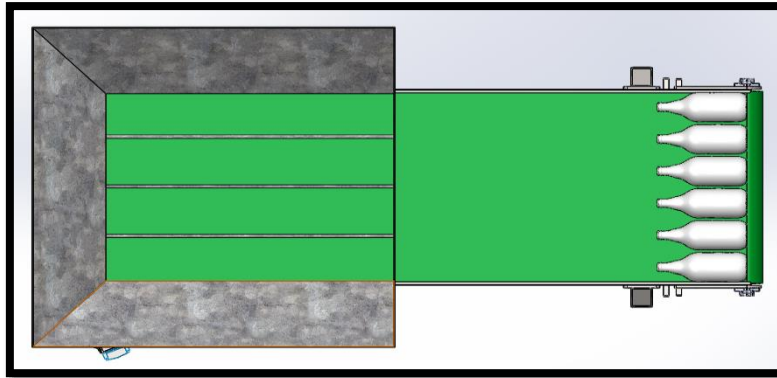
Vista en planta de CTA. Disposición de botellas ejemplo
